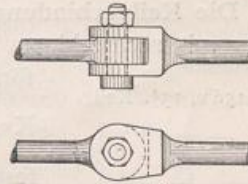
u. 148. Verbindung zweier Rundeisenstangen.
